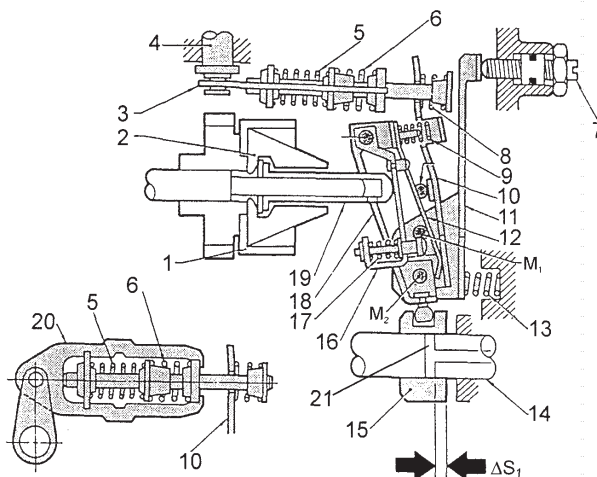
Схема двухрежимного регулятора. Режим пуска дизеля: 1 - держатель грузов; 2 - грузы регулятора; 3 - серья; 4 - ось рычага управления; 5 - пружина номинального режима; 6 - пружина частичного режима; 7 - регулировочный винт максимальной подачи; 8 - демпферная пружина; 9 - пружина холостого хода минимального режима; 10 - силовой рычаг; 11 - регулировочный рычаг; 12 - пружина пусковой подачи; 13 - поддерживающая пружина; 14 - плунжер ТНВД; 15 - дозирующая муфта; 16 - рычаг отрицательного корректора; 17 - пружина отрицательного корректора; 18 - пусковой рычаг; 19 - муфта регулятора; 20 - корпус пружин регулятора; 21 - отверстия отсечки подачи; шарниры рычажной системы регулятора: M_1 - система рычагов в этой точке поддерживается двумя подвижными пальцами, установленными в рычаге 2; M_2 - общая ось рычагов пускового и корректора; ΔS_1 - ход дозирующей муфты.
